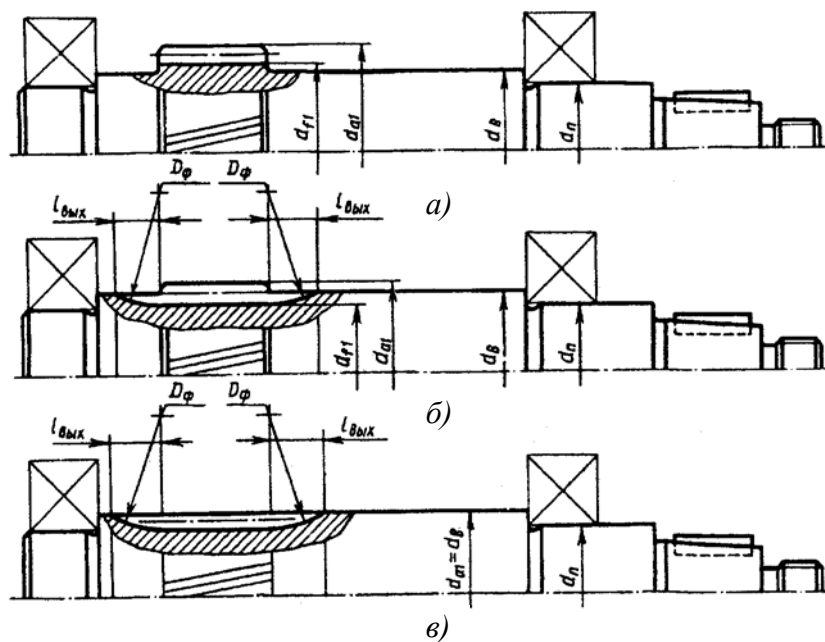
Конструкция вала – шестерни цилиндрической зубчатой передачи
